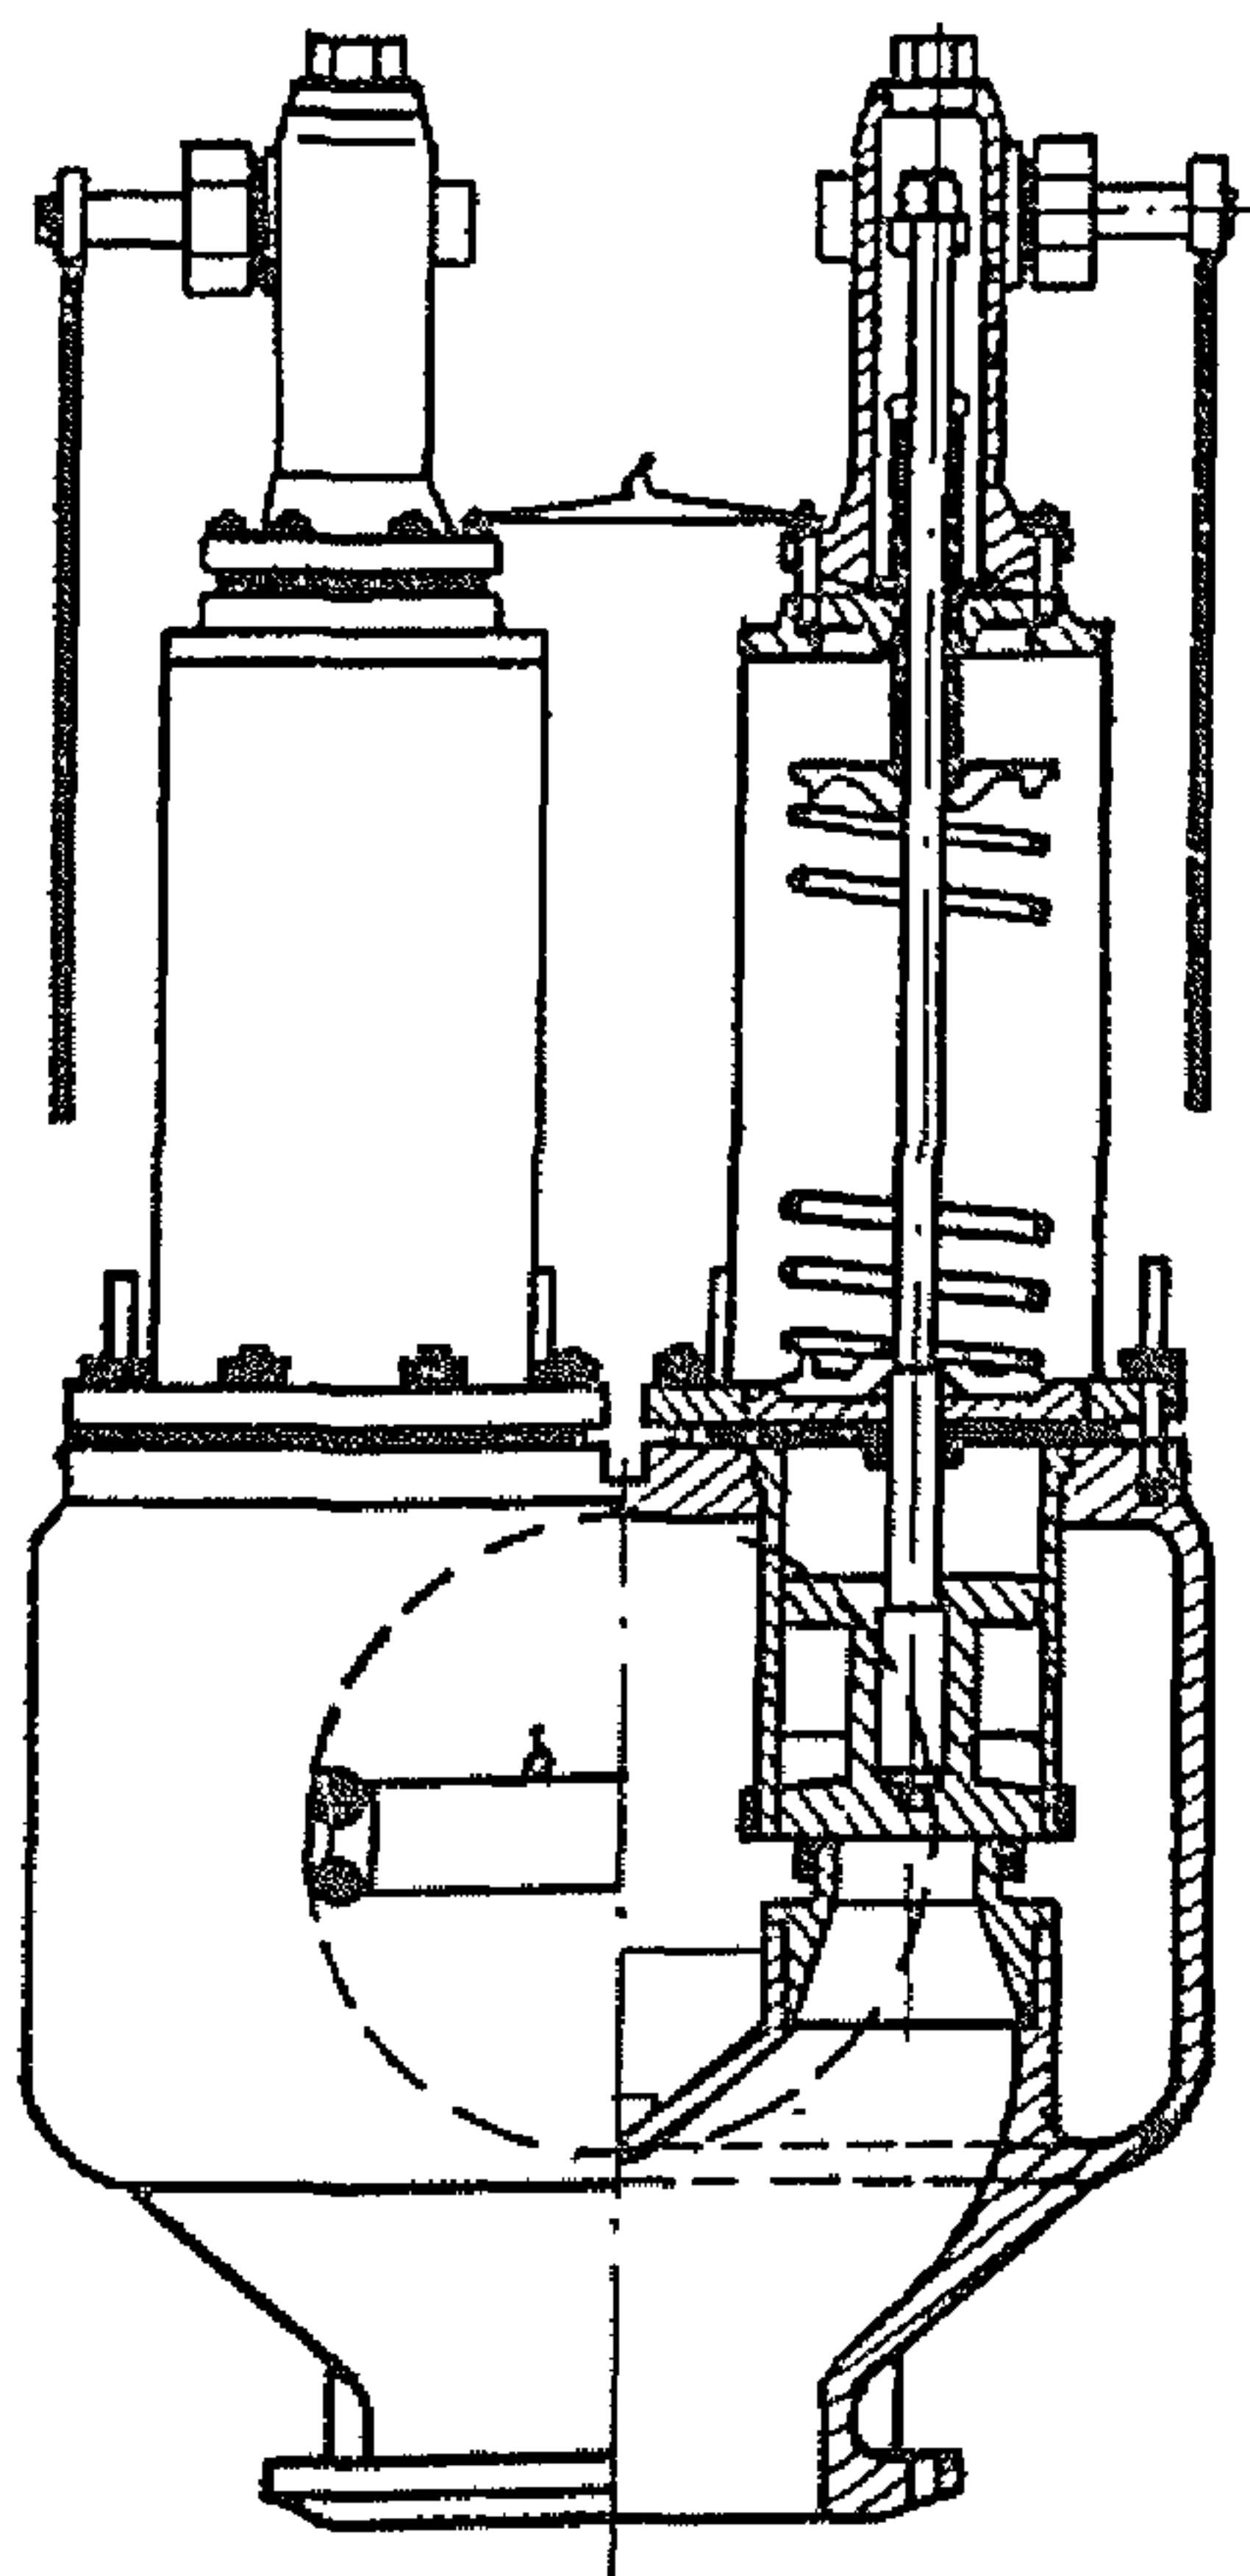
9. Клапан предохранительный пружинный сдвоенный типа 2СППК-200-16.
